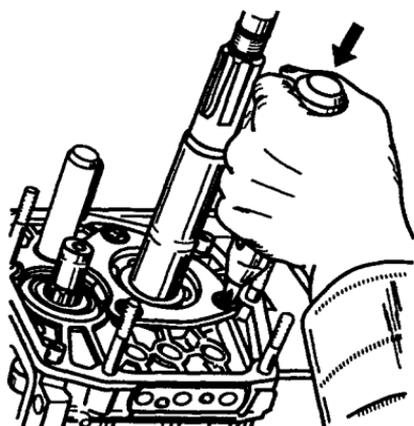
Отвинчивание винтов крепления стопорной пластины промежуточного подшипника вторичного вала ударной отверткой (стрелкой указано направление удара молотком)
